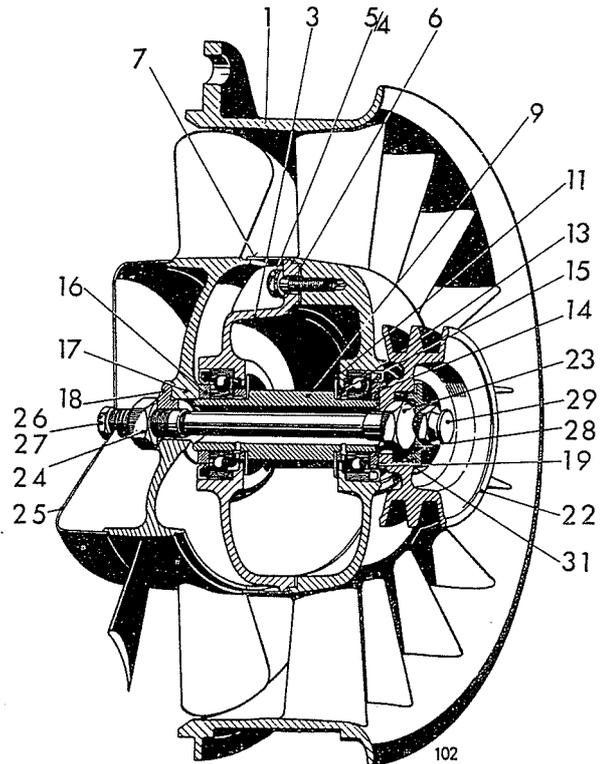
Kühlluftgebläse (zweiteilig) F/A4-6L 514
